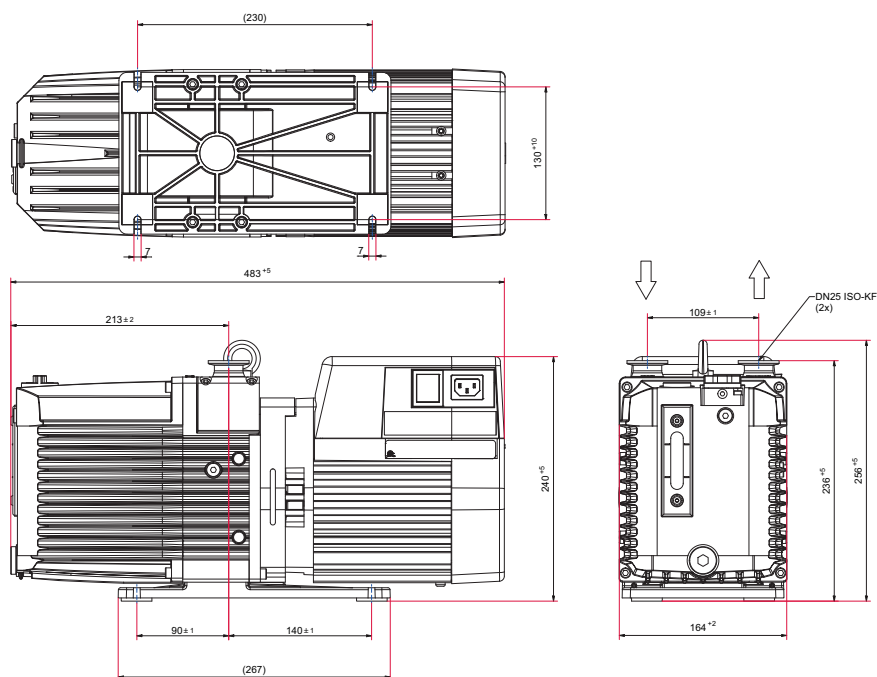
Dimensions DuoVane 22 avec moteur monophasé
